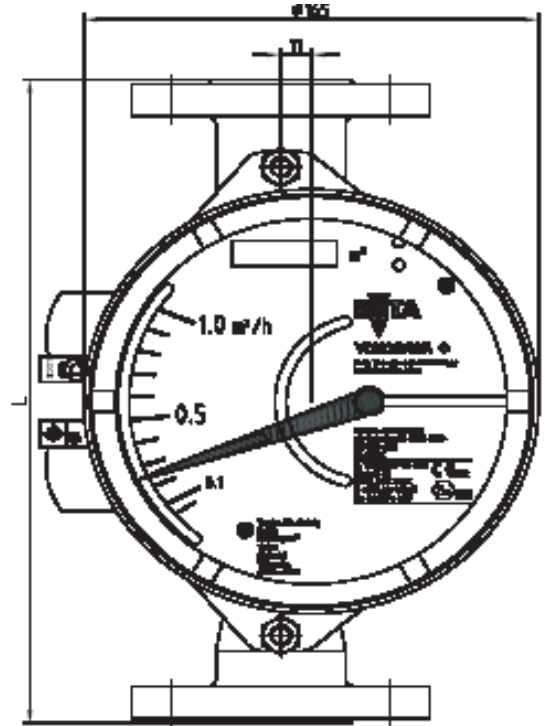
RAMC, вид спереди. Корпус типа 91
